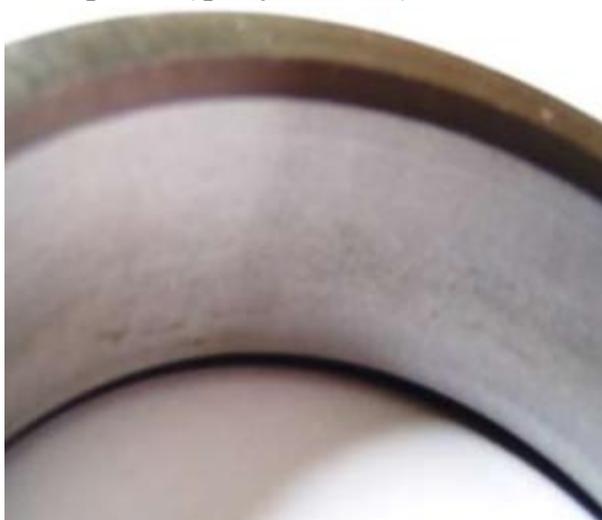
Матова поверхня внутрішнього кільця підшипника при нерухомій посадці на вал
